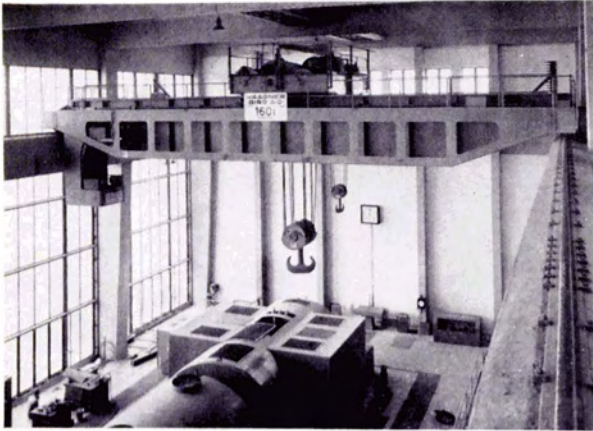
160-t-Maschinenhauslaufkran in geschweißter Vollwandträgerbauweise mit Rahmennebenenträgern, geliefert für das E-Werk Simmering der Wiener Stadtwerke
